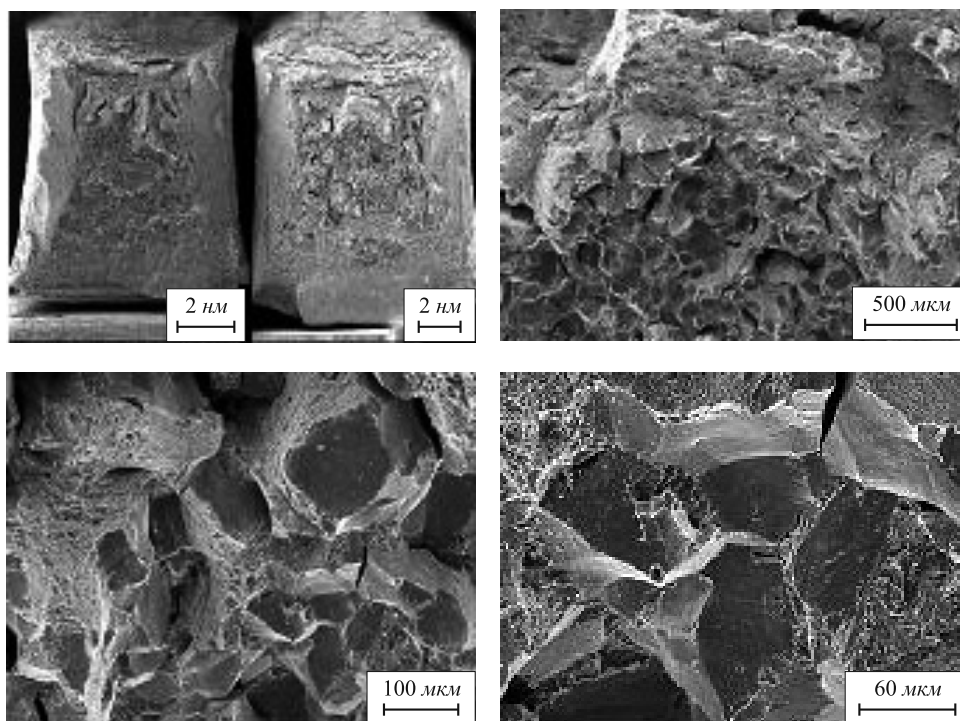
Поверхность разрушения образцов стали 32ХГМРА после термической обработки по схеме закалки 1000 °С и отпуска 680 °С (1,5 ч)
